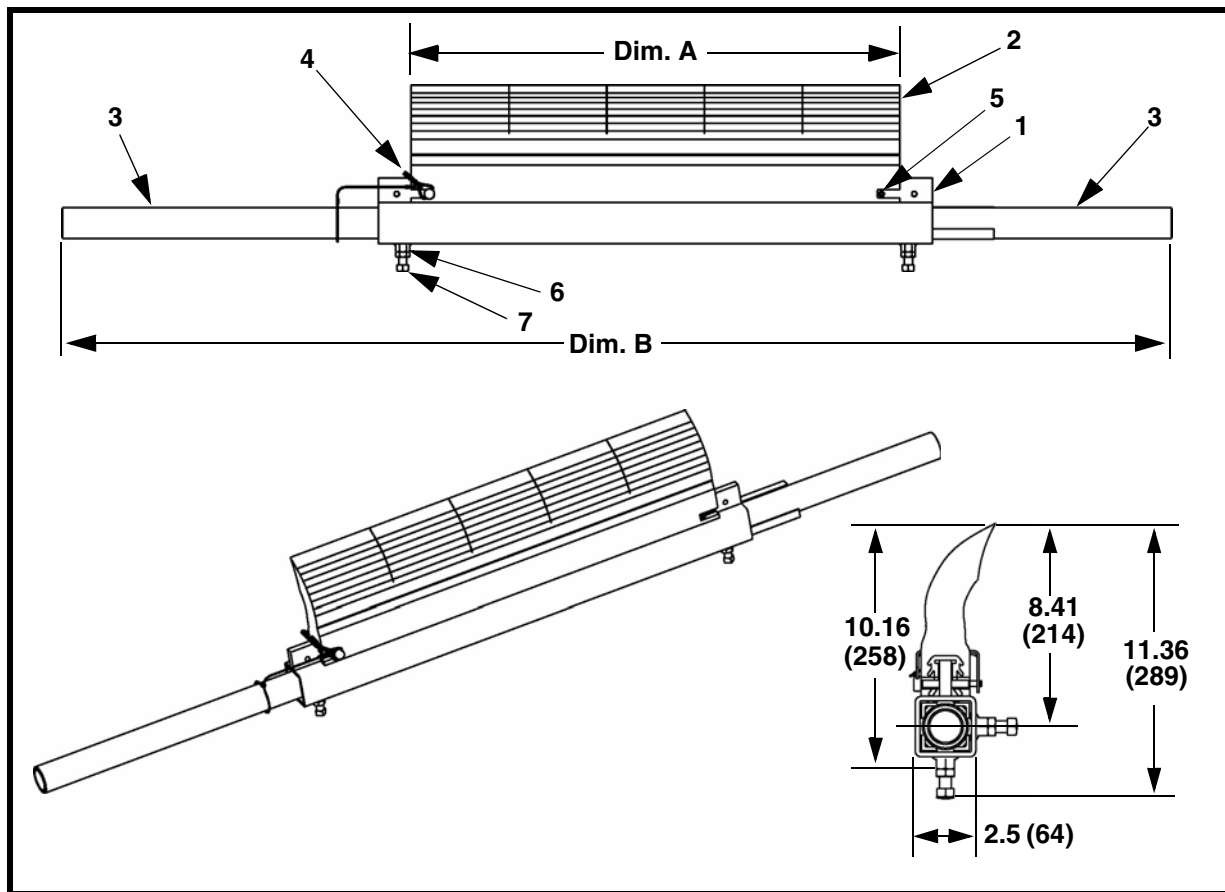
Conjunto do Limpador HD Martin® QC1™, P/N 36898-XXXXXXXX
